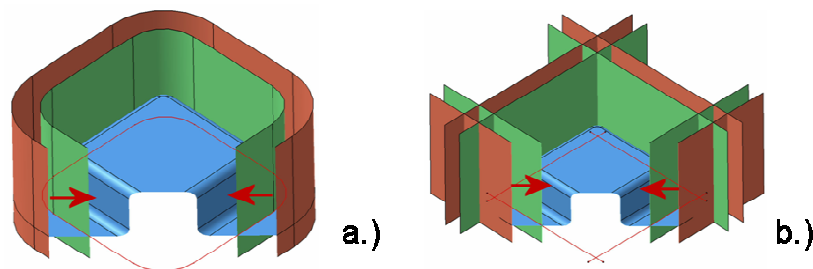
Schema der Konstruktion assoziativer Beschnittflächen und Schweißpunktlinien
